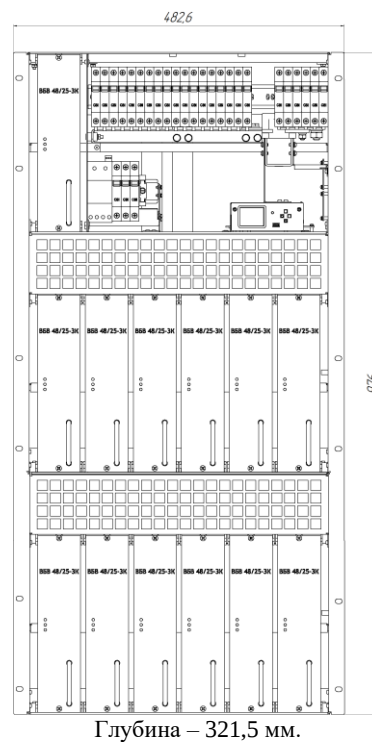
Габаритный чертеж УЭПС-3К 48/100-44 (ВЭ), УЭПС-3К 60/80-44
